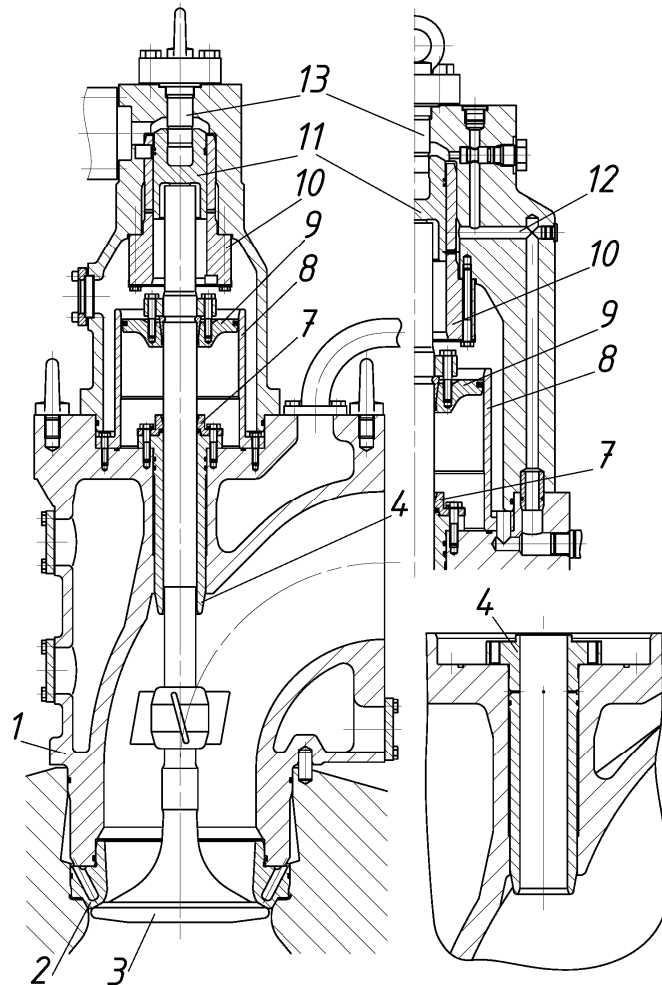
Клапанний вузол дизеля RTA 72 U з гідропневматичним приводом клапана. 1 – корпус; 2 – сідло клапана; 3 – клапан; 4 – напрямна втулка клапана; 5 – пневматична пружина; 6 – тарілка пружин; 7 – сальник штока клапана; 8 – робочий циліндр пневматичної пружини; 9 – пневматичний поршень; 10 – гідравлічний циліндр привода клапана; 11 – гідравлічний поршень привода клапана; 12 – дренажний канал збору протечек; 13 – упор гідрогальма клапана
